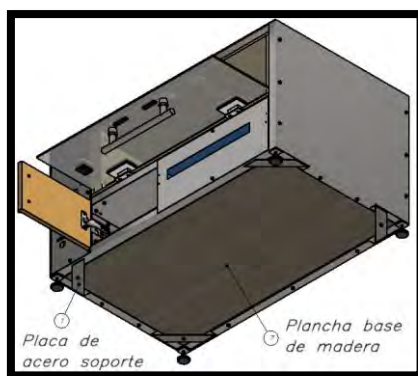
Plancha base de madera y placa de acero soporte.
